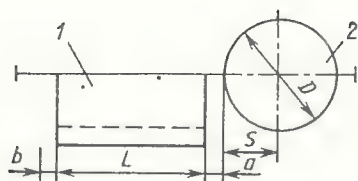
Расположение фрезы и детали (образующая детали и ось фрезы расположены на одной прямой):
